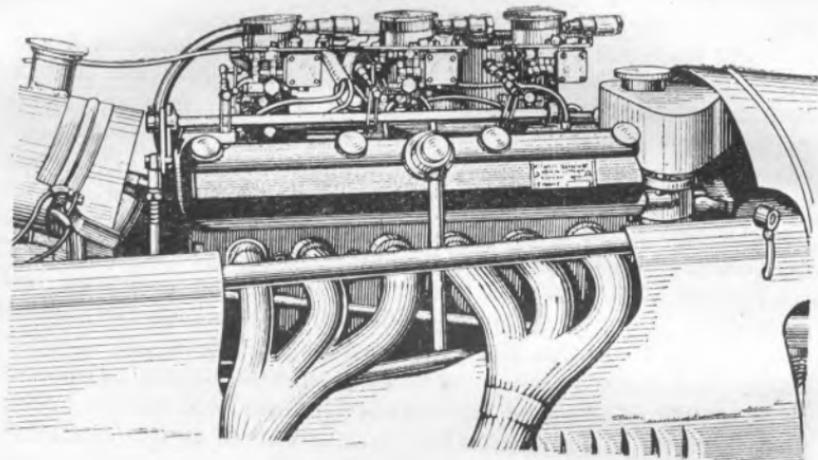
Установка трех карбюраторов с падающим потоком на шестицилиндровом двигателе
